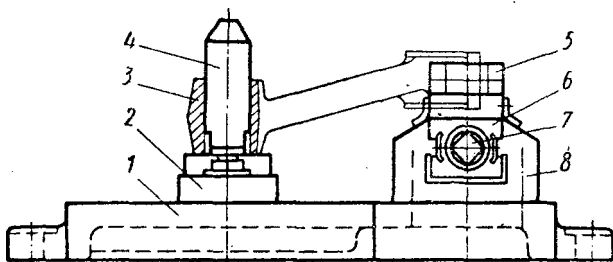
Универсально-наладочное приспособление для фрезерования бобышек у рычагов
